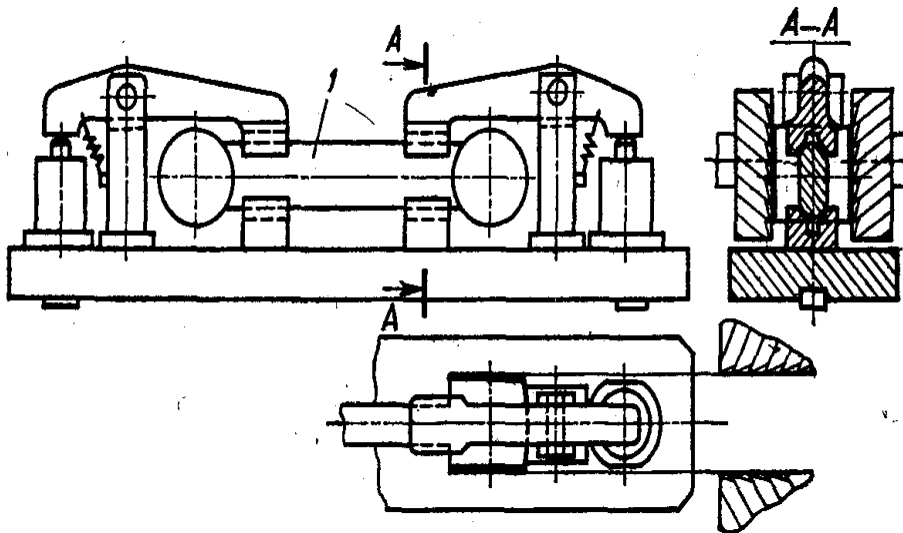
Схема базирования заготовки рычага при обработке торцев
